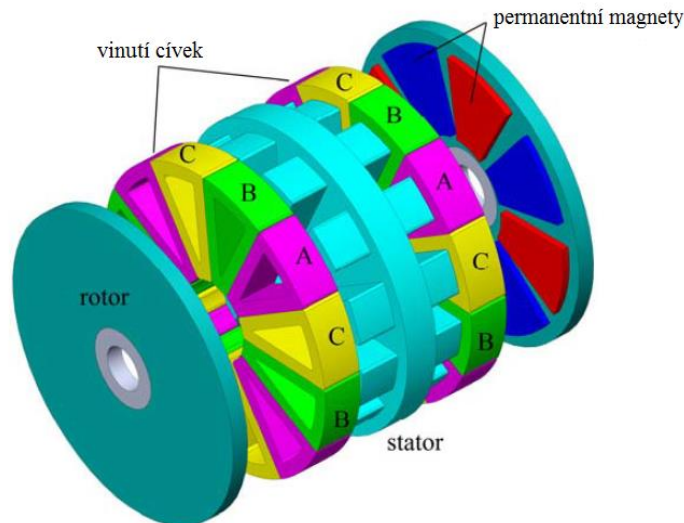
Konstrukce rotoru s magnety uvnitř nemagnetického rotoru [2]
